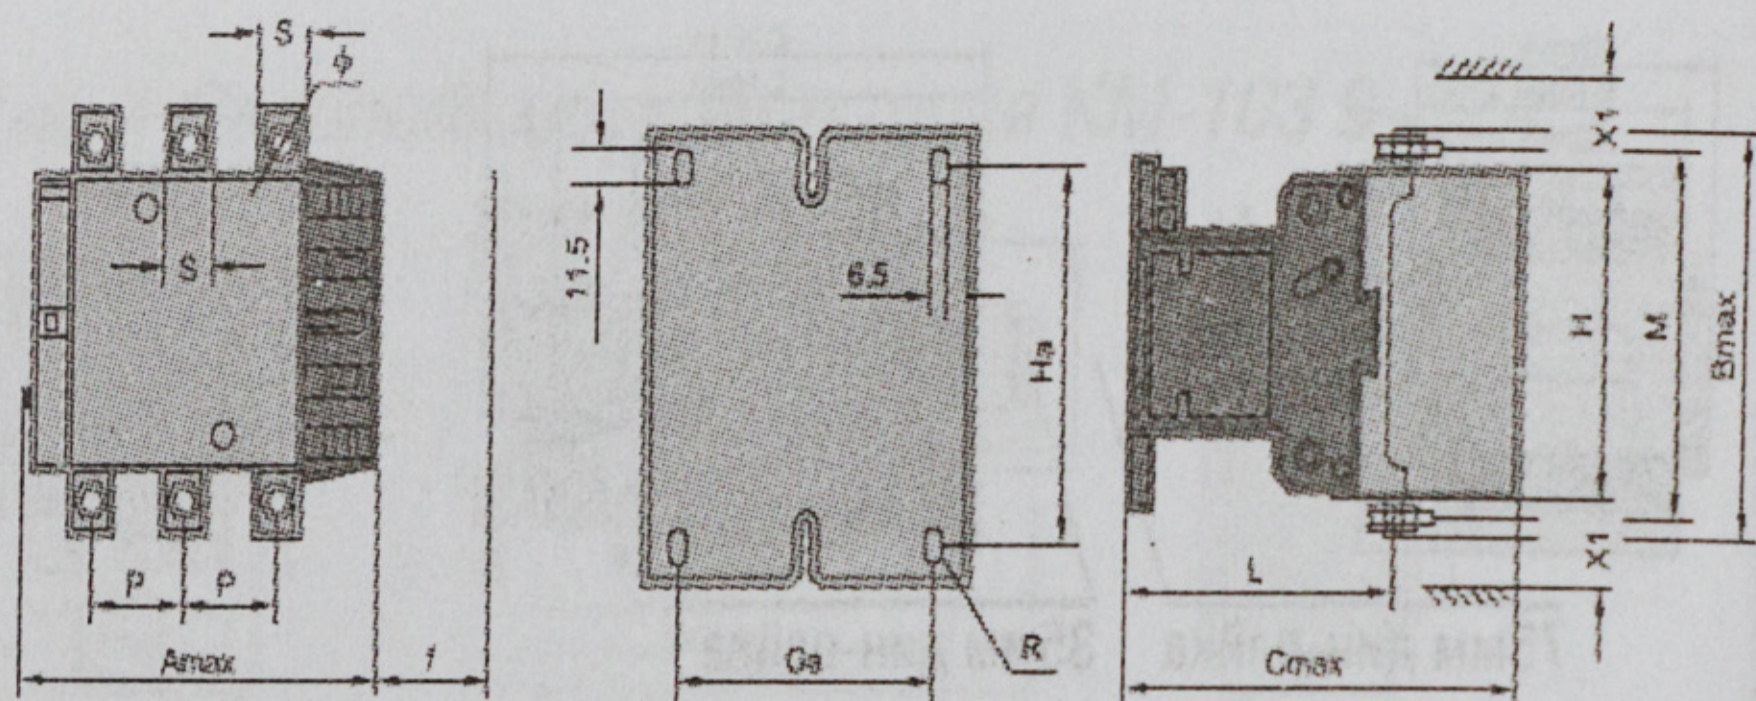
Внешний вид контакторов КМ-103 400-500А
